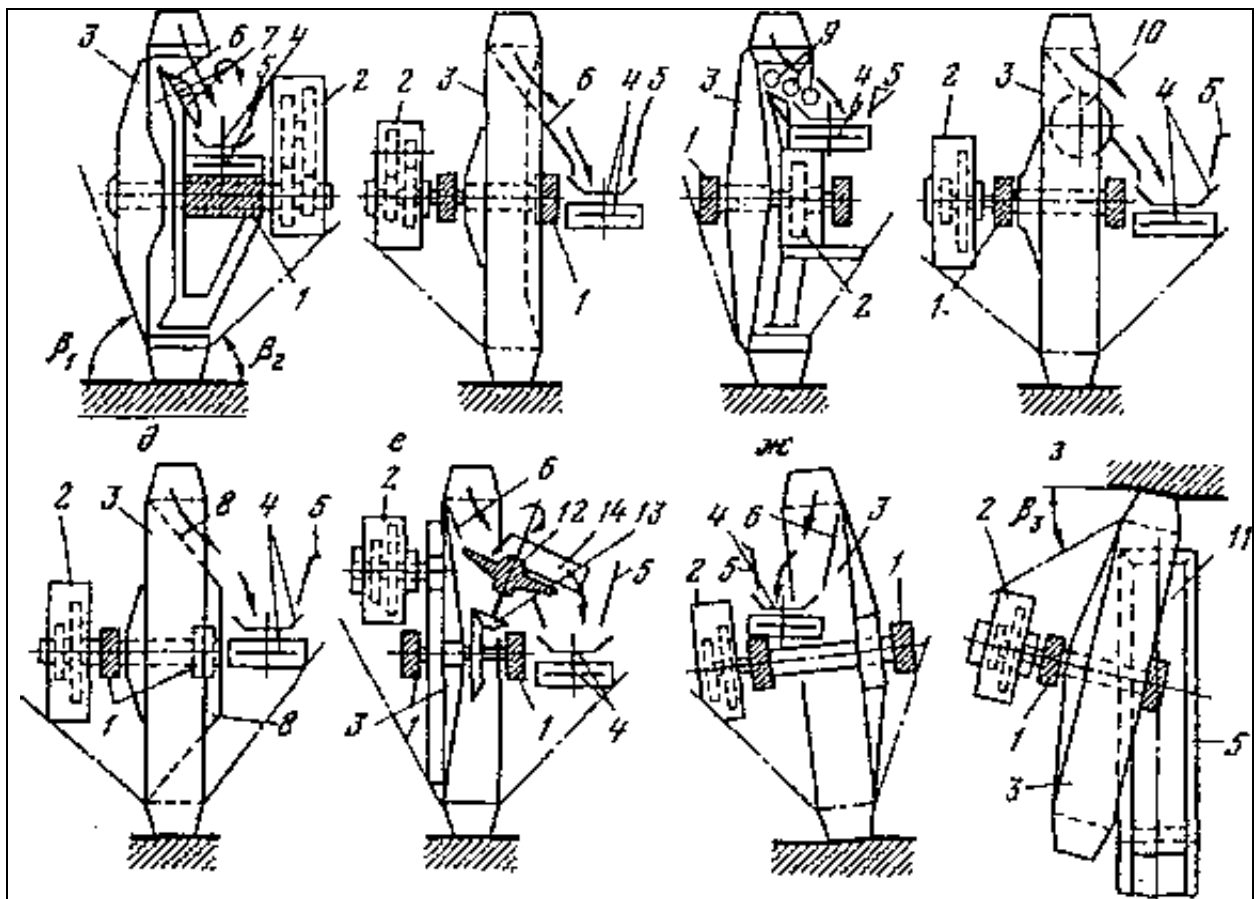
Схеми приймально-живильних пристроїв роторних виконавчих органів: 1 - опора роторного колеса; 2 - редуктор; 3 - роторне колесо; 4 - стрічка конвеєра роторної стріли; 5 - бортик конвеєра; 6 - лоток; 7 - скребок; 8 – конус, що обертається; 9 - ролик; 10 - барабан; 11 - стрічковий живильник; 12 - тарільчастий живильник; 13 - конічна передача; 14 - нерухомий скребок
